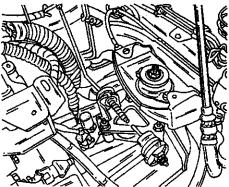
Установочное положение левой опоры двигателя (со стороны коробки передач). Гайка имеет момент затяжки 65 нм.
